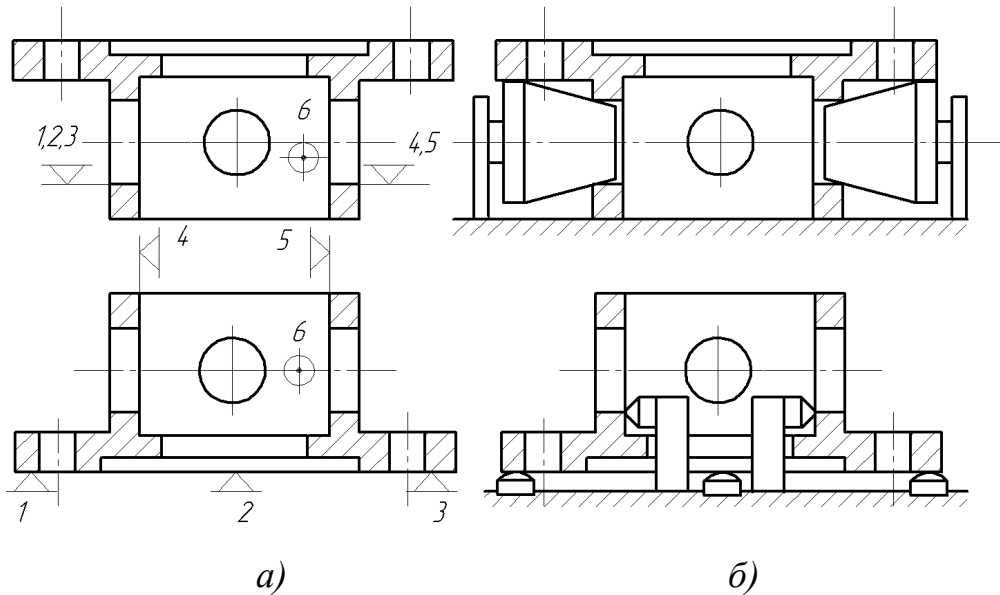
Схеми базування корпусних деталей коробчастого типу:
